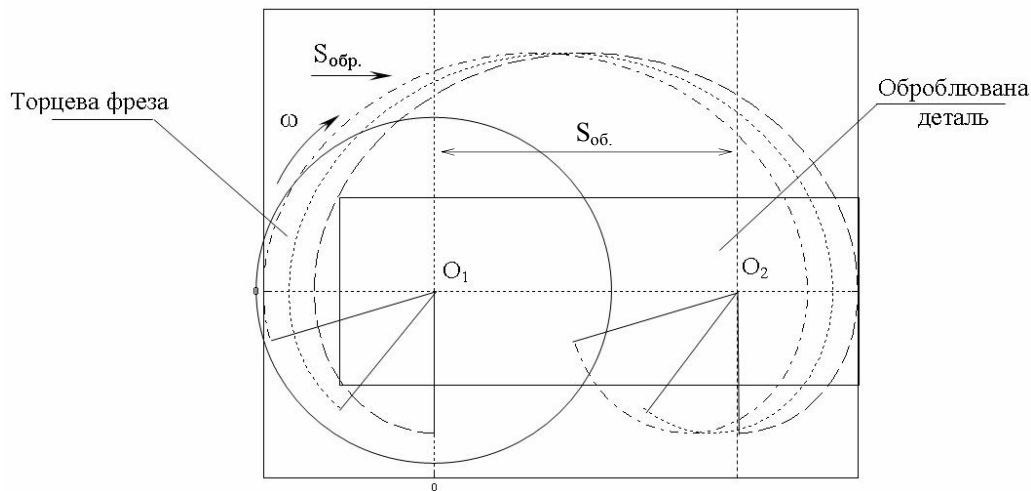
Траєкторії руху вершин ножів торцевої фрези
